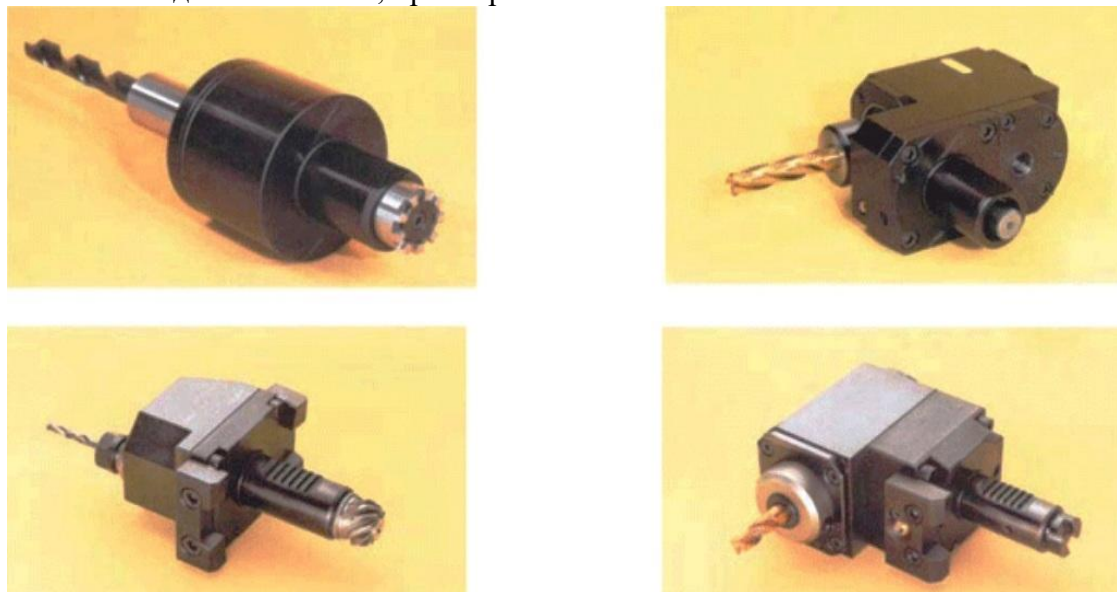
Приводний інструмент для верстатів токарної групи з ЧПК
